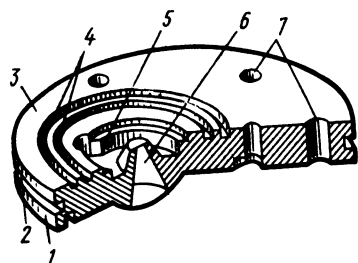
Нижняя торцевая стенка резонатора металлического клистрона:
